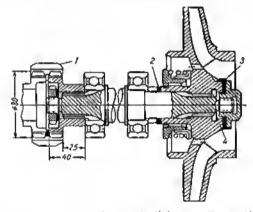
Arbol en conjunto con el rotor de álabes y cojinetes (dibujo de composición)
